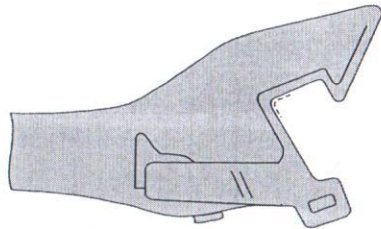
Контроль угла сопряжения ударной и боковой поверхностей большого зуба
